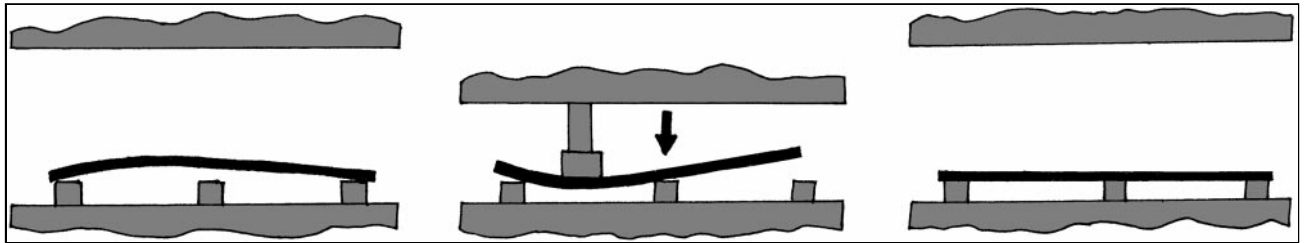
Richten von Blechteilen mit einer hydraulischen Presse
